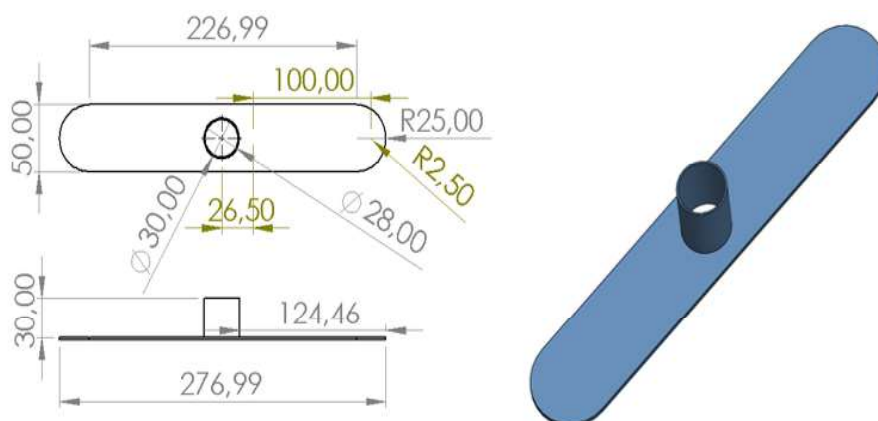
Diseño 3D de la placa superior con sus medidas.
